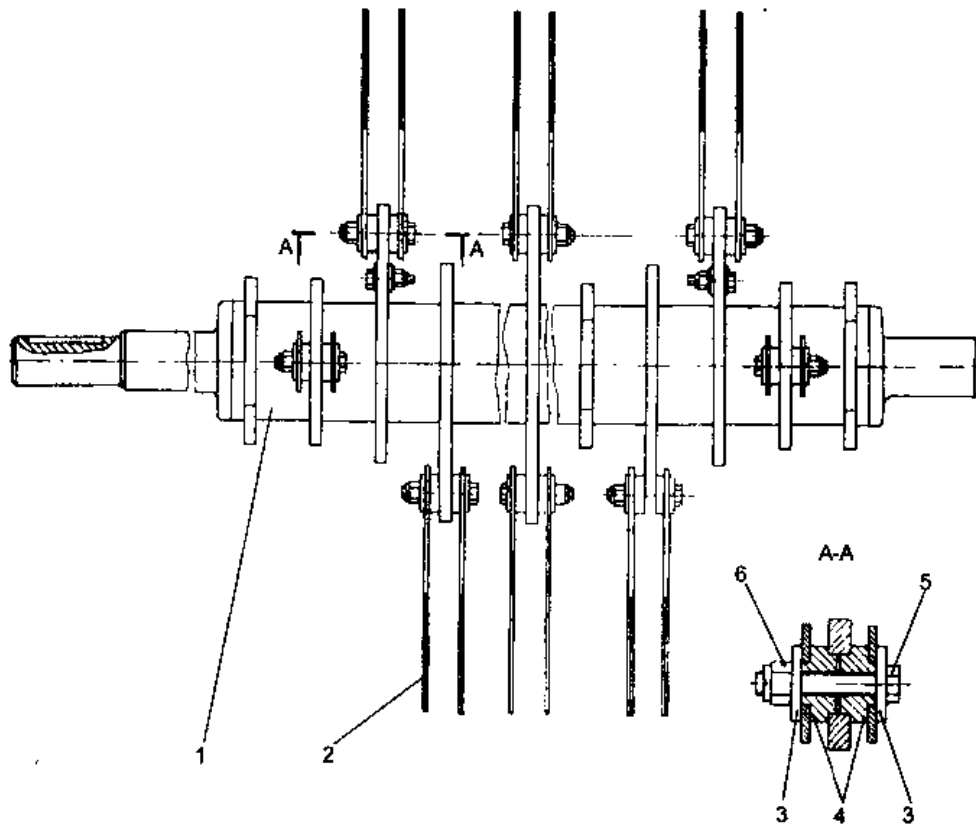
Барабан измельчающий: 1 – вал барабана; 2 – нож; 3 – шайбы; 4 – втулки; 5 – болт; 6 – гайка самоконтрящаяся
